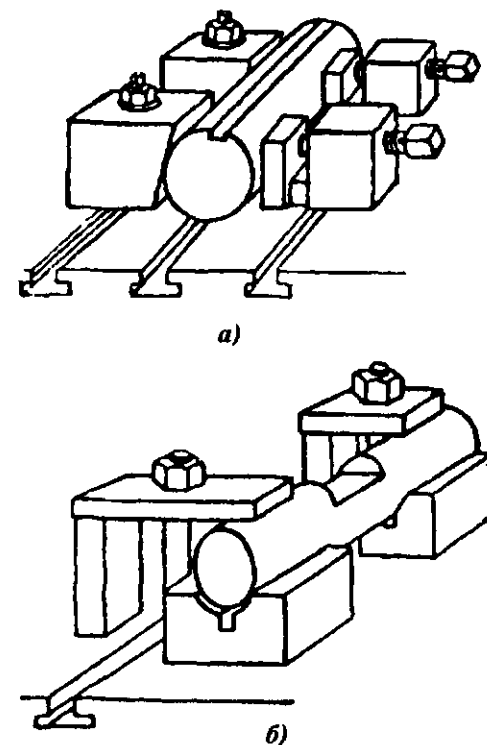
Схема установки и закрепления деталей типа валов: а – непосредственно на столе станка; б – на призмах
